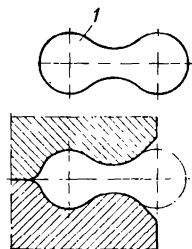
Подкатной ручей для заготовки с двумя симметрично расположенными наборами: I — заготовка
